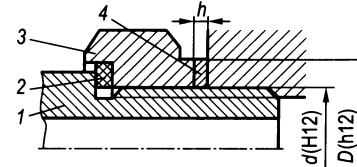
Уплотнение трубопроводов плоскими прокладками:
